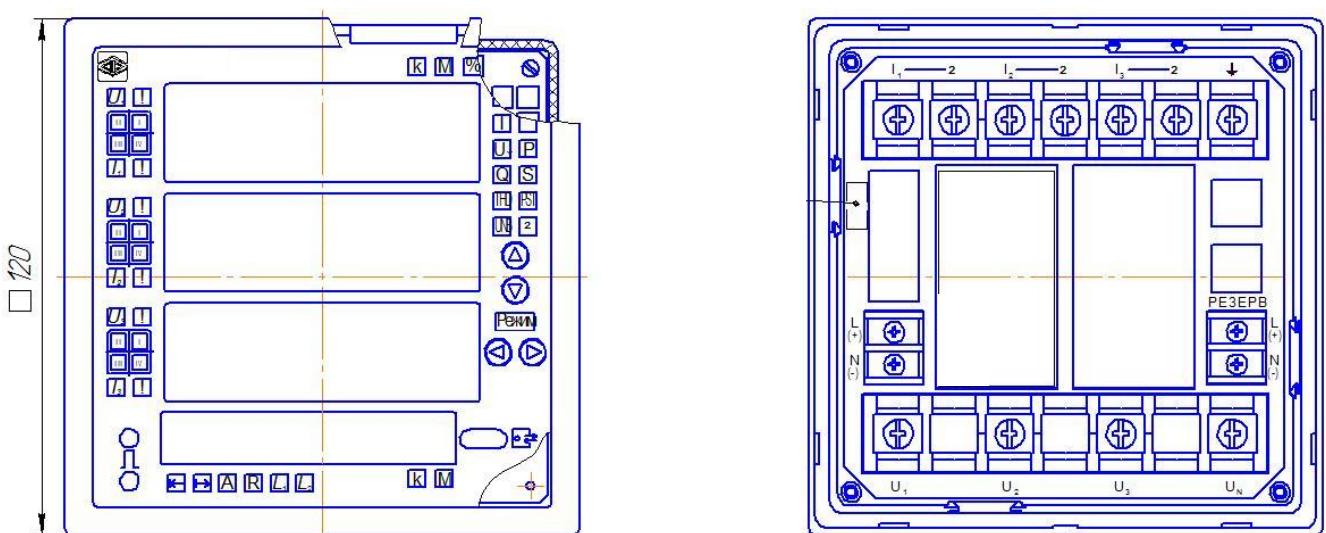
Габаритные размеры приборов ЩМК120С
